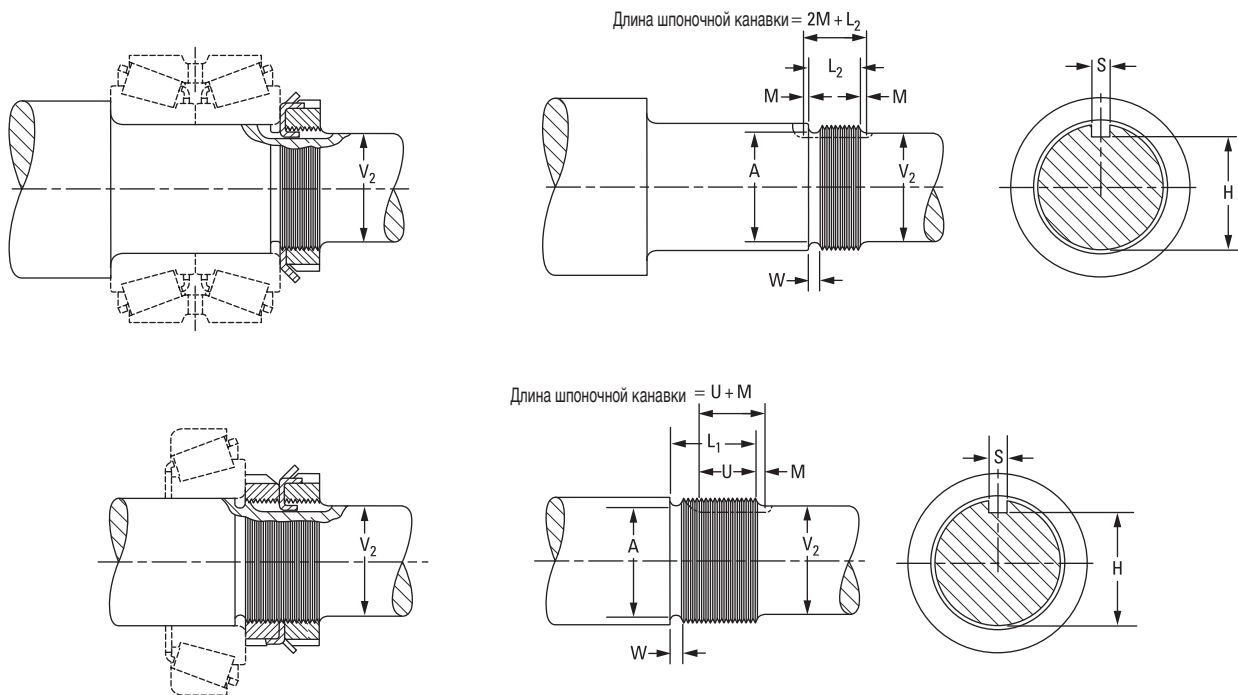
Стопорные гайки, стопорные шайбы и стопорные шайбы с внутренним выступом.
